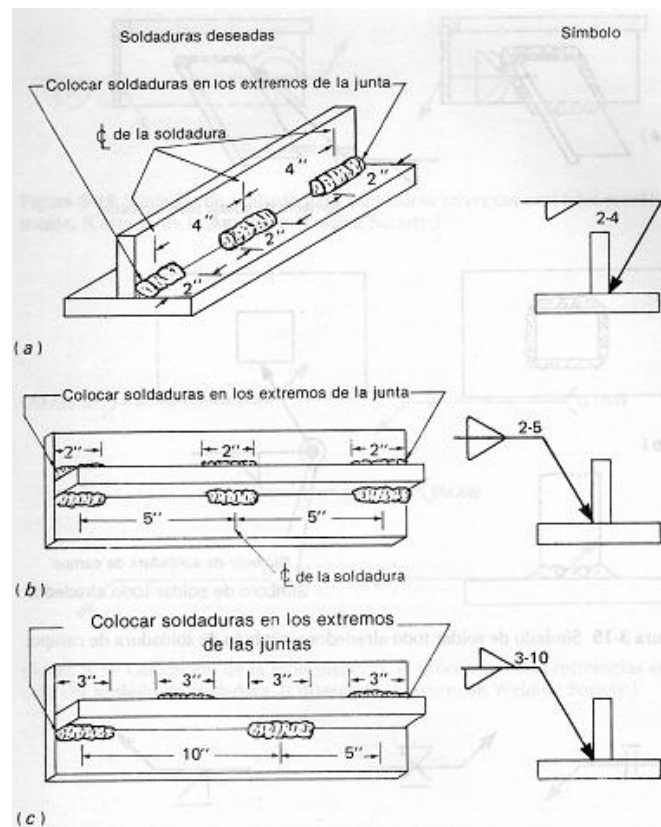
Símbolos de soldadura en los que se especifican la longitud y el paso de las soldaduras: a) soldadura intermitente; b) soldadura intermitente de cadena; c) soldadura intermitente escalonada.
